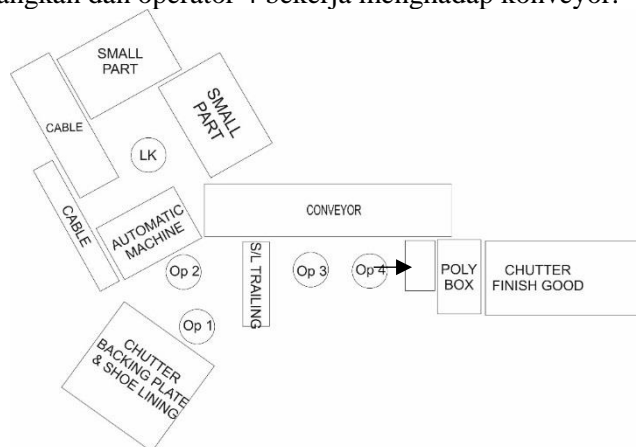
Layout produksi brake assembly line 2 sebelum kaizen
